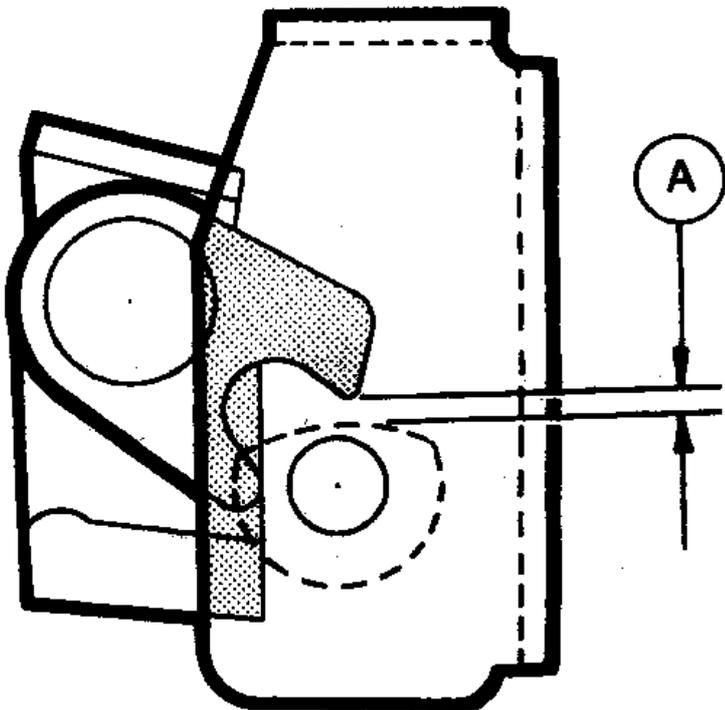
Проверка регулировки фиксатора дверного замка (Разд.7)
